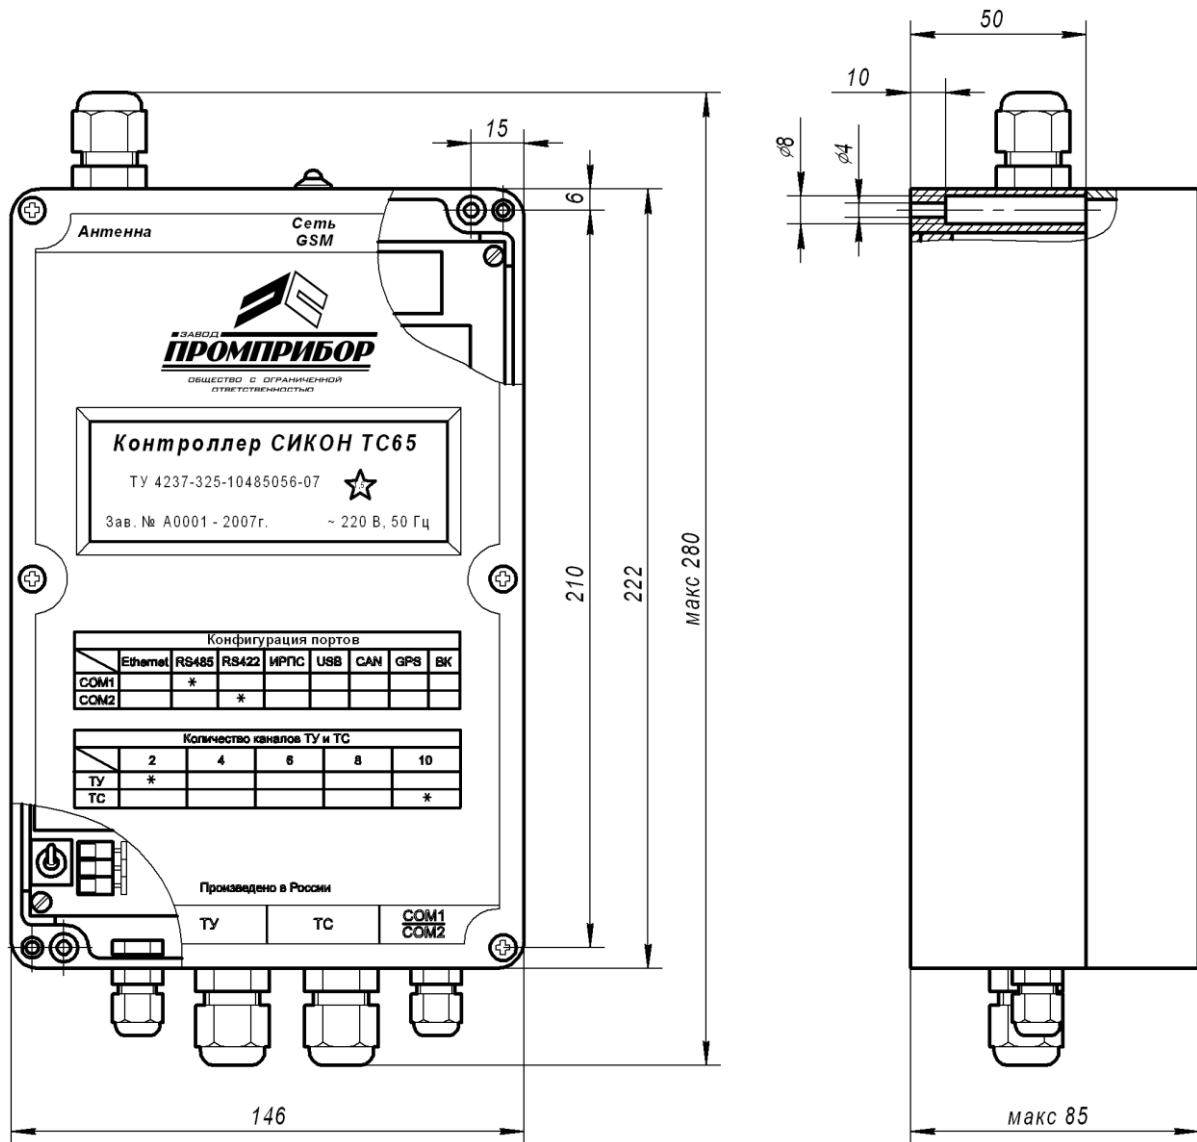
Габаритные и установочные размеры контроллера СИКОН ТС65 в металлическом корпусе
